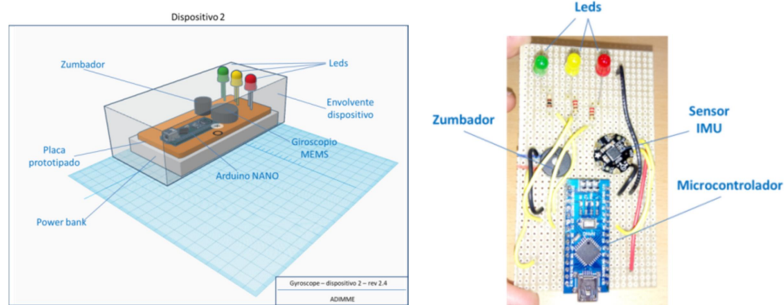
Boceto 3D Dispositivo 2 (izqda.) y montaje de Dispositivo 2 en placa de soldadura (dcha.).
